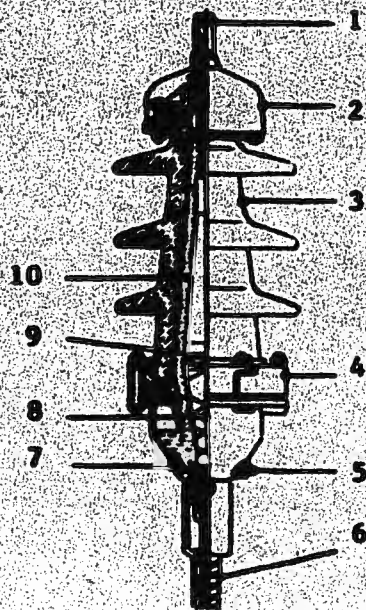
Disposición de un terminal para intemperie y cable con aislamiento de papel impregnado de envolturas (cable triplomo).
